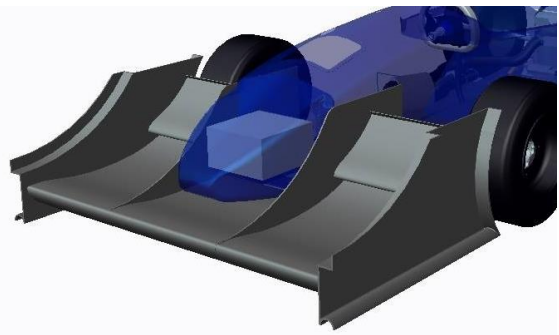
Komplexe Seitenplatten auch am Fahrzeug der University of Auckland, AUS [AUC14]
